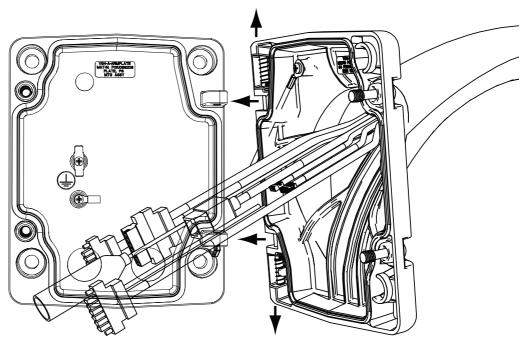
Raccordez le bras de fixation à la plaque de montage
